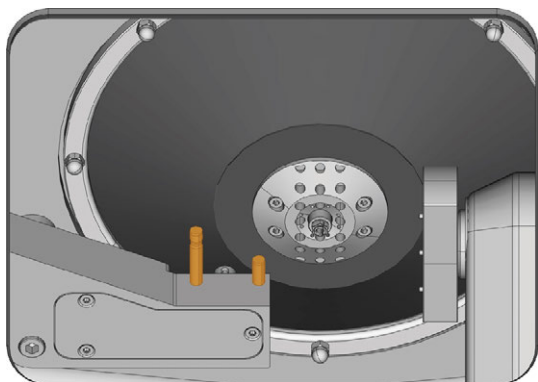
Die Stifte des Werkzeugmagazinhalters (orange markiert)
